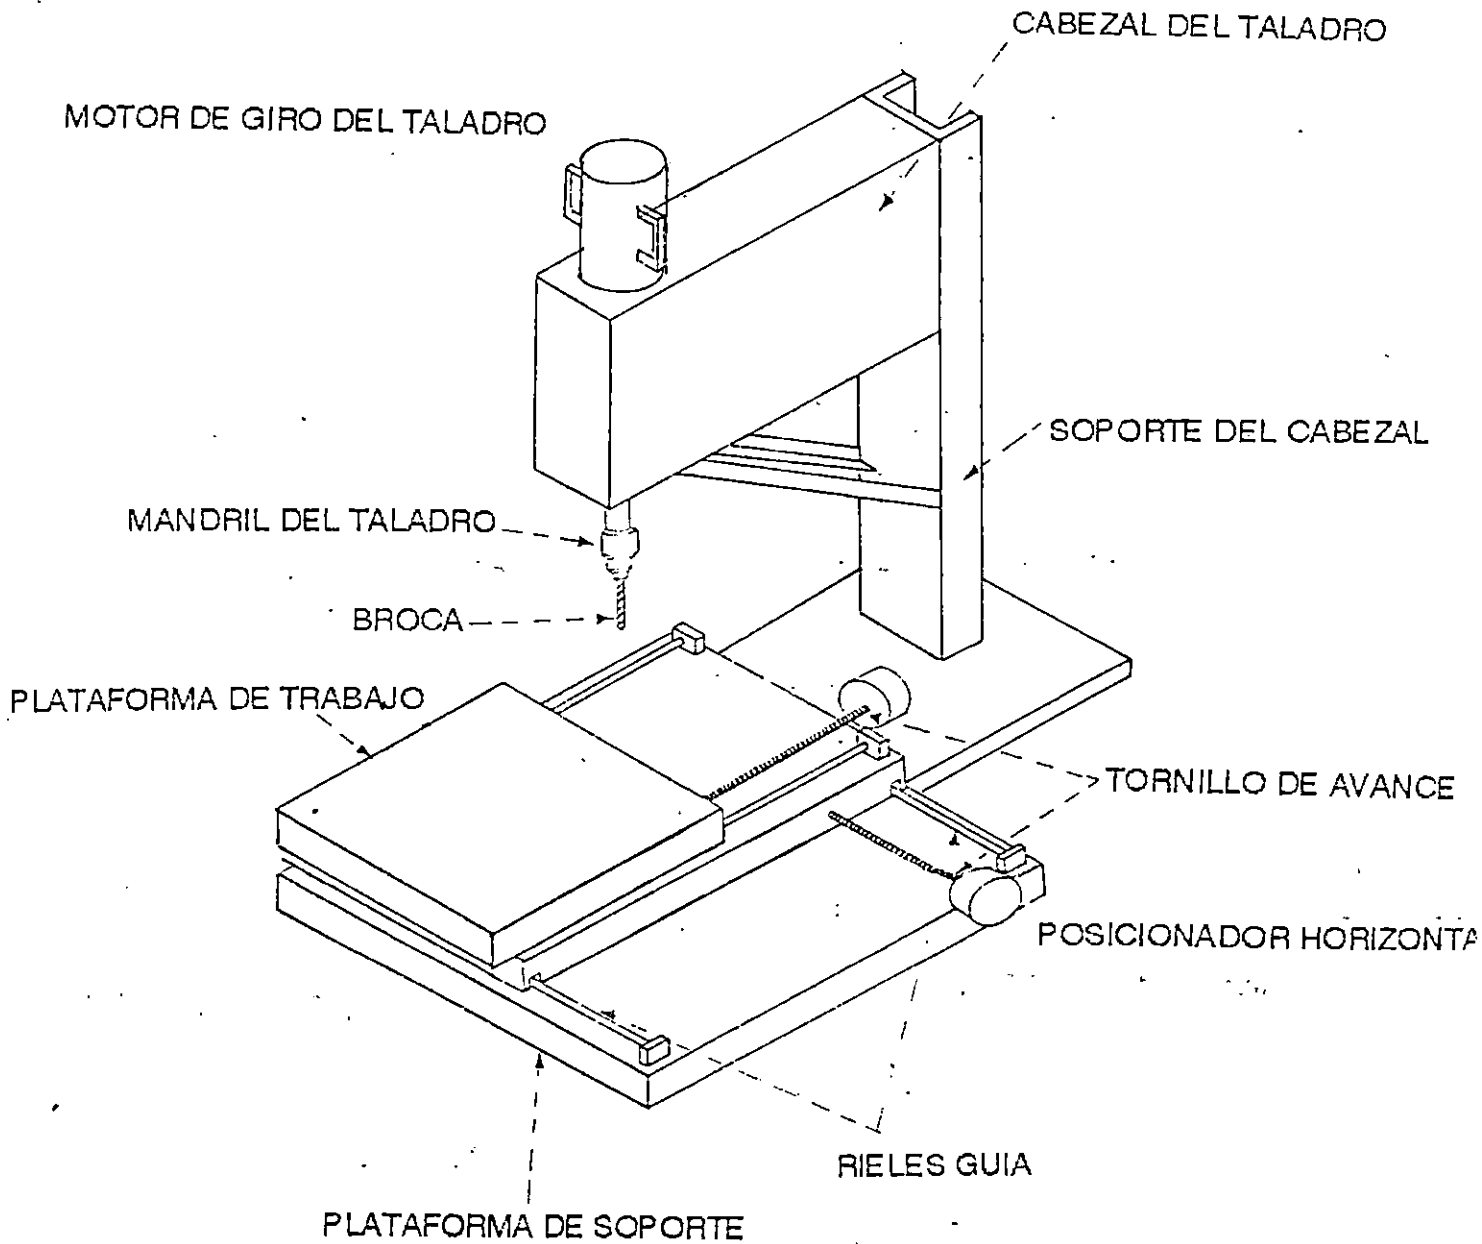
Bosquejo de la máquina taladradora a implementar.
